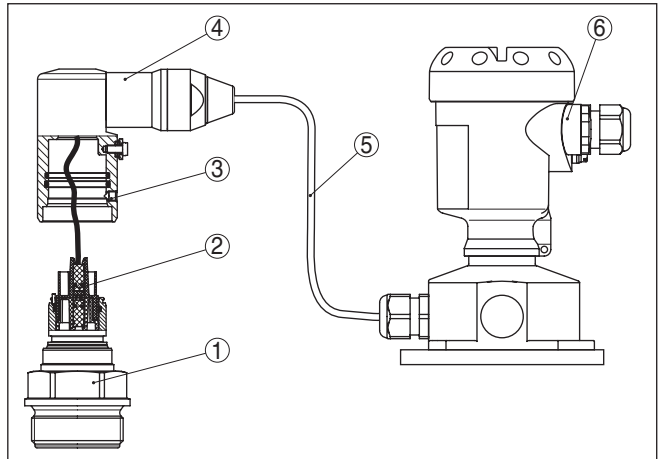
IPT-2x in IP 68-Ausführung 25 bar und seitlichem Kabelabgang, externes Gehäuse
